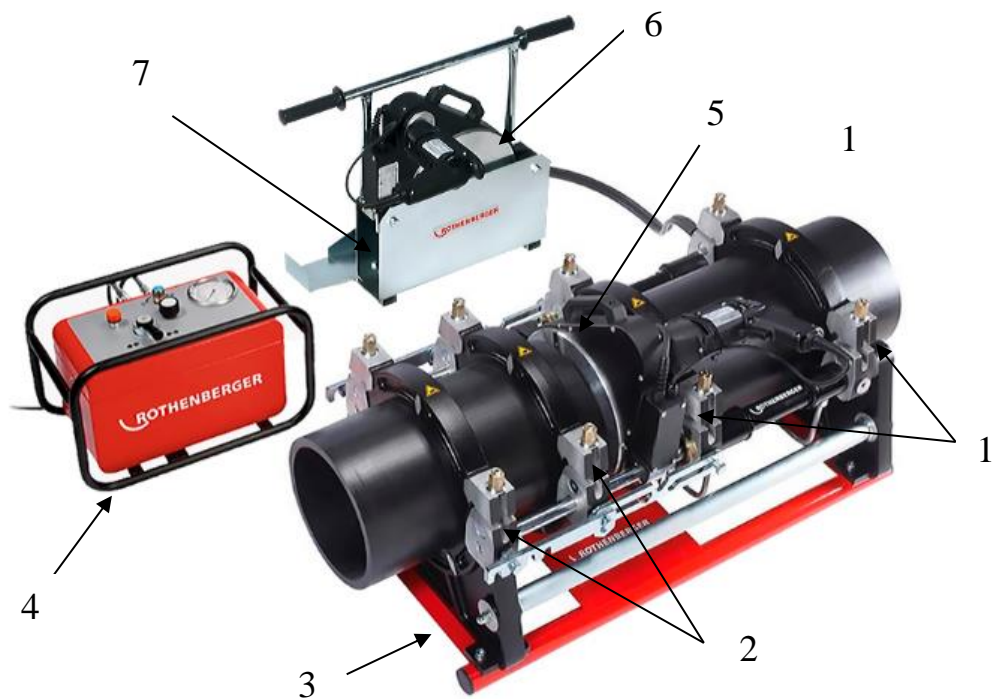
Состав оборудования с гидравлическим приводом для стыковой сварки [42]
